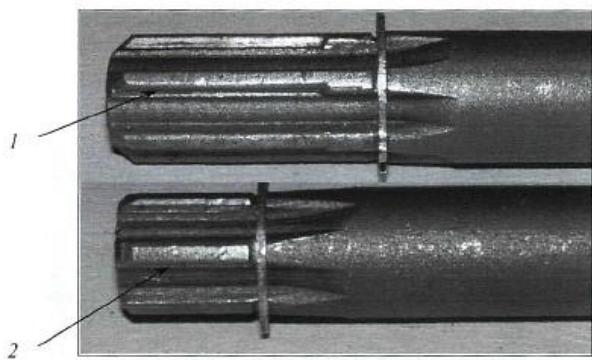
Изношенные поверхности шлицев валика 700A.17.00.038-3 (1 – шлицевая часть вала, соединяемая с шестерней конического редуктора; 2 – шлицевая часть вала, соединяемая с втулкой привода насоса)
